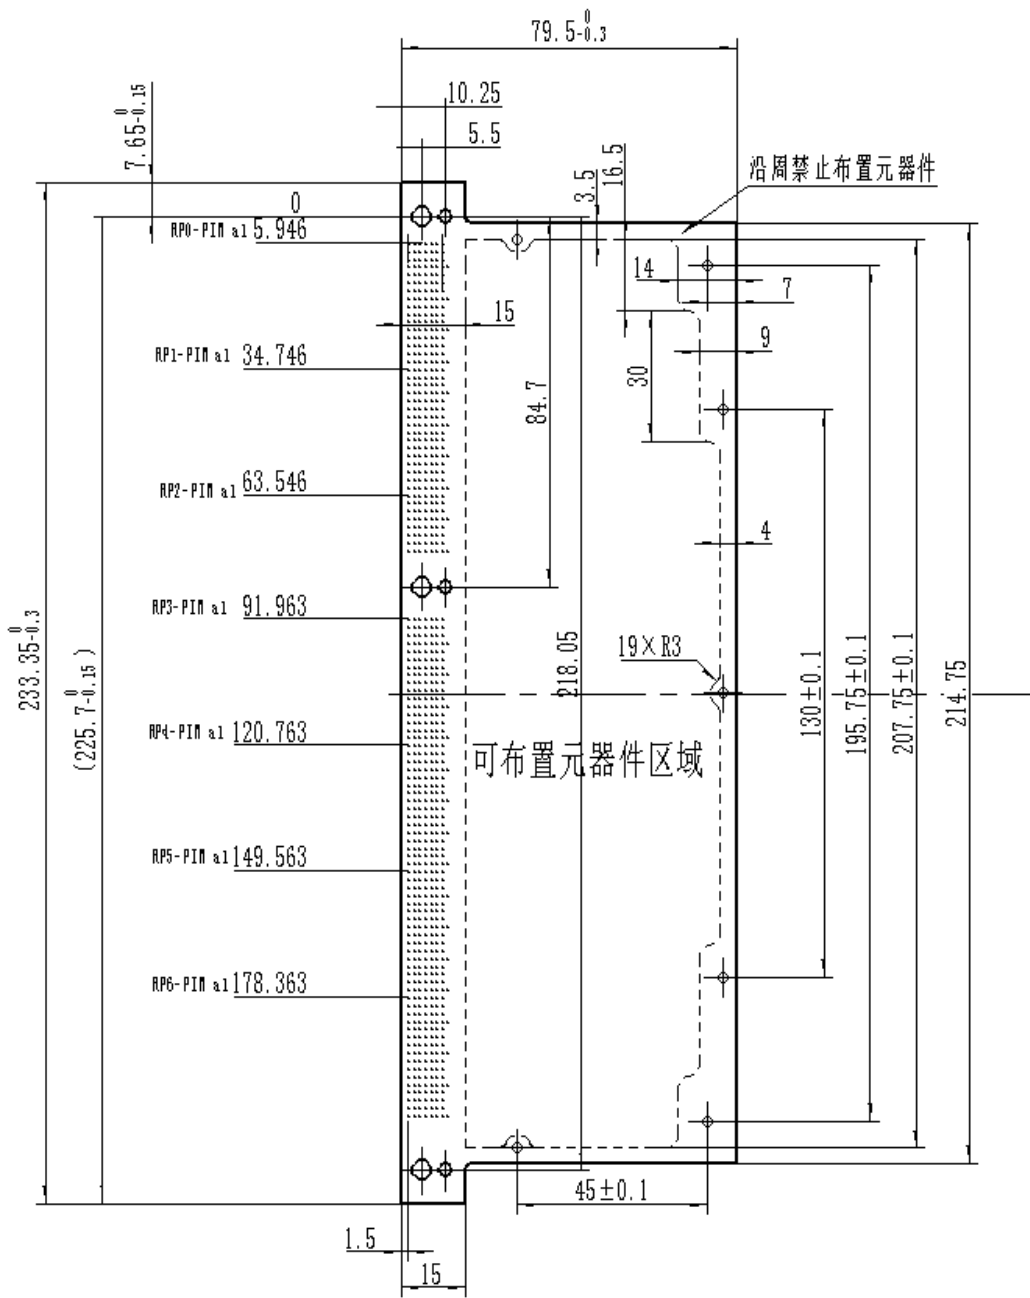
6U 标准导冷后插模块 PCB 板的安装尺寸
